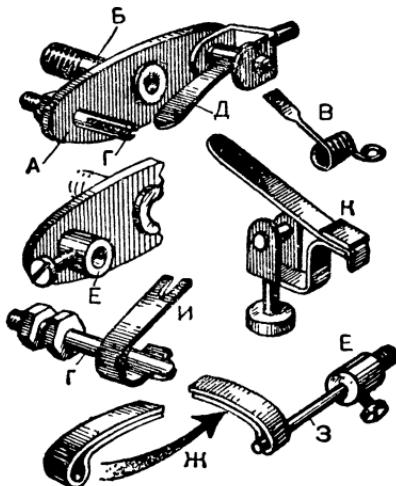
Поворотный щеткодержатель и щетки к нему: А — пластина щеткодержателя — полоска из фибры; Б — штепельное гнездо; В — щетка из гарнированной медной проволоки; Г — укороченная ножка от вилки; Д — щетка из гарнированной латуни или бронзы; Е — контакт от выключателя; Ж — рессорная щетка; З — проволочный стержень; И — разрезная щетка; К — вариант крепления щетки из листового материала.
